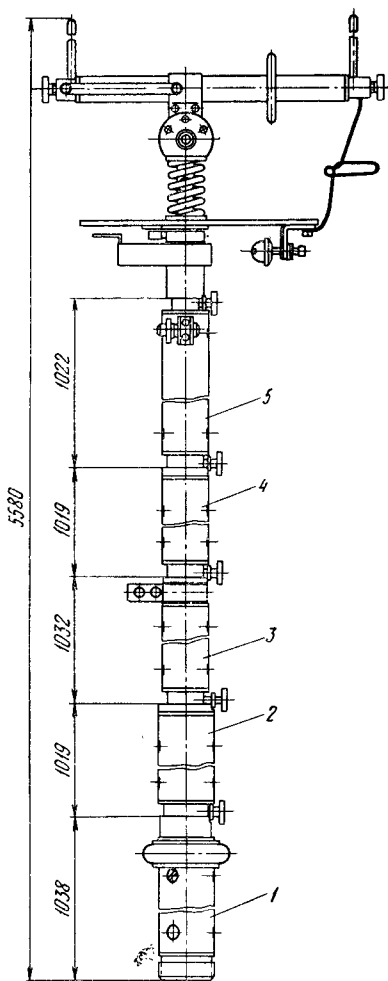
Общий вид измерительной штанги для контроля изоляторов.
